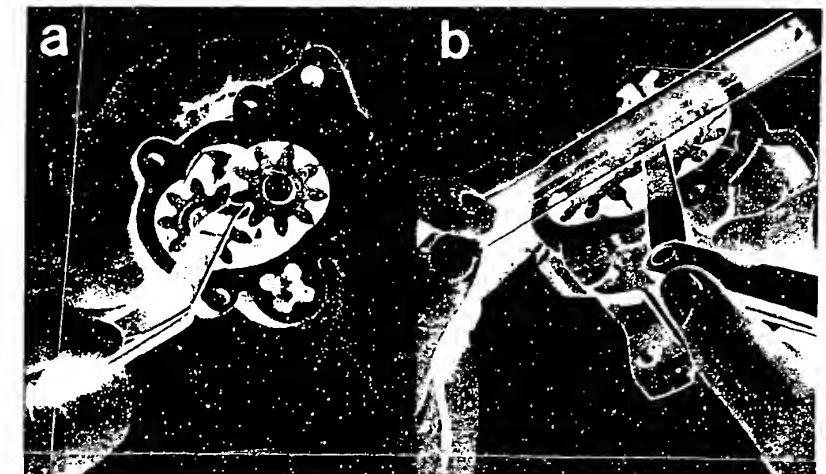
Das Messen des Zahnflankenspiels (a) und des Axialspiels (b) an der Zahnrad-Ölpumpe.
